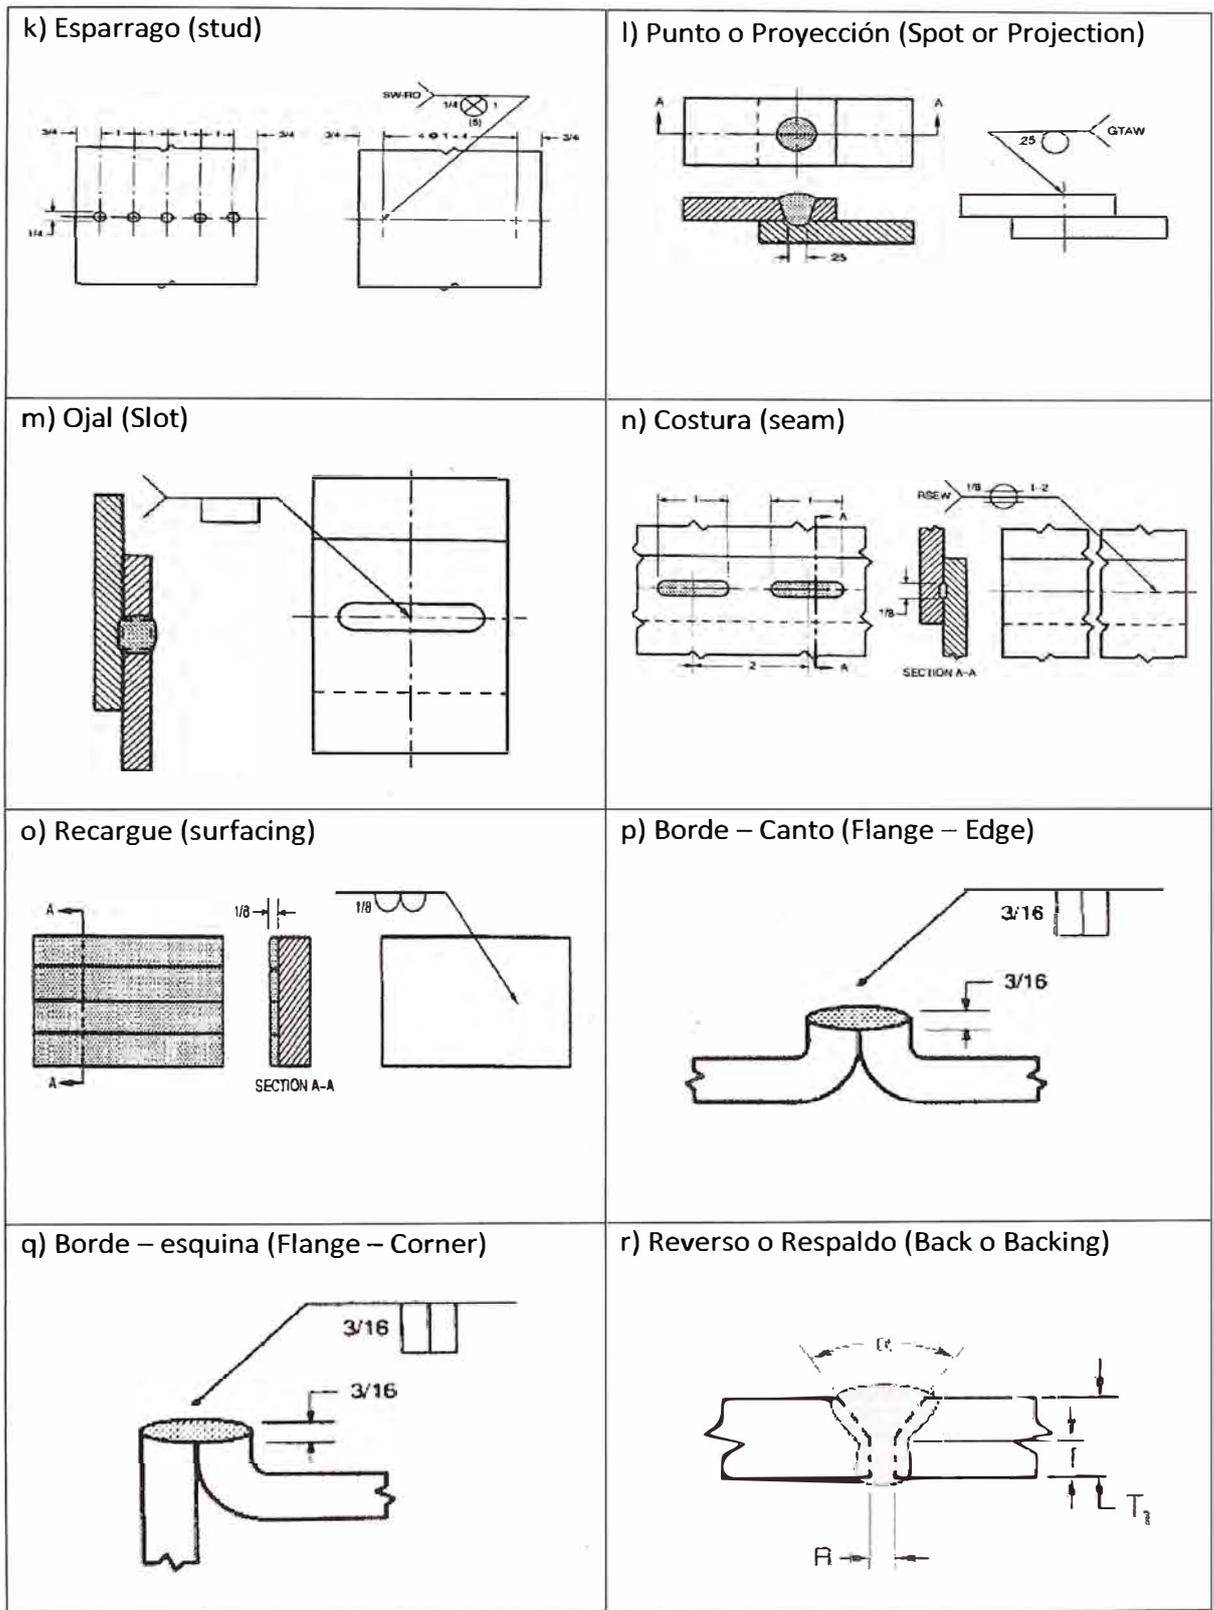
Tipos de Soldadura Empleados en el País
